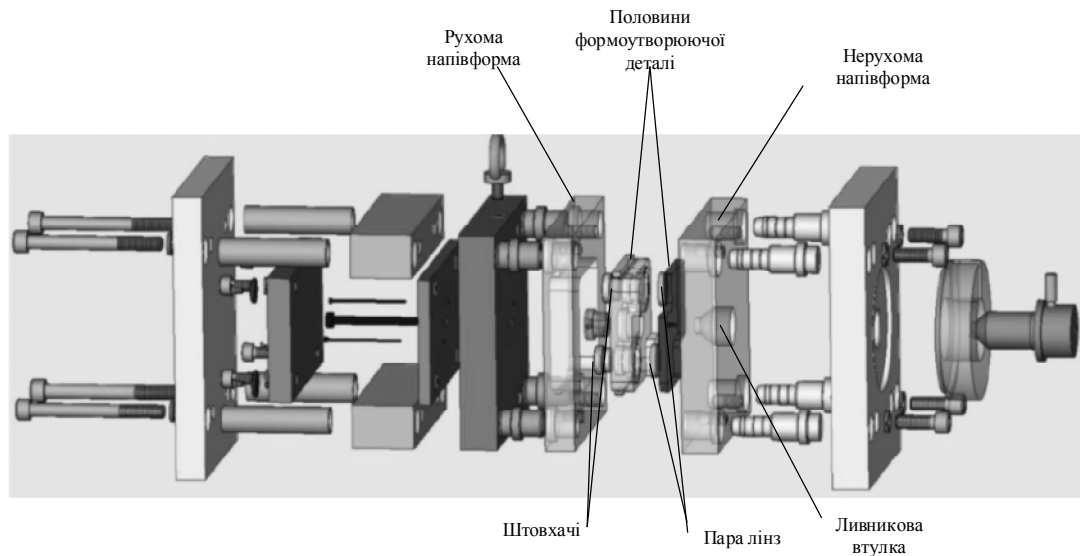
3D модель ливарної форми з виливком полімерної лінзи
